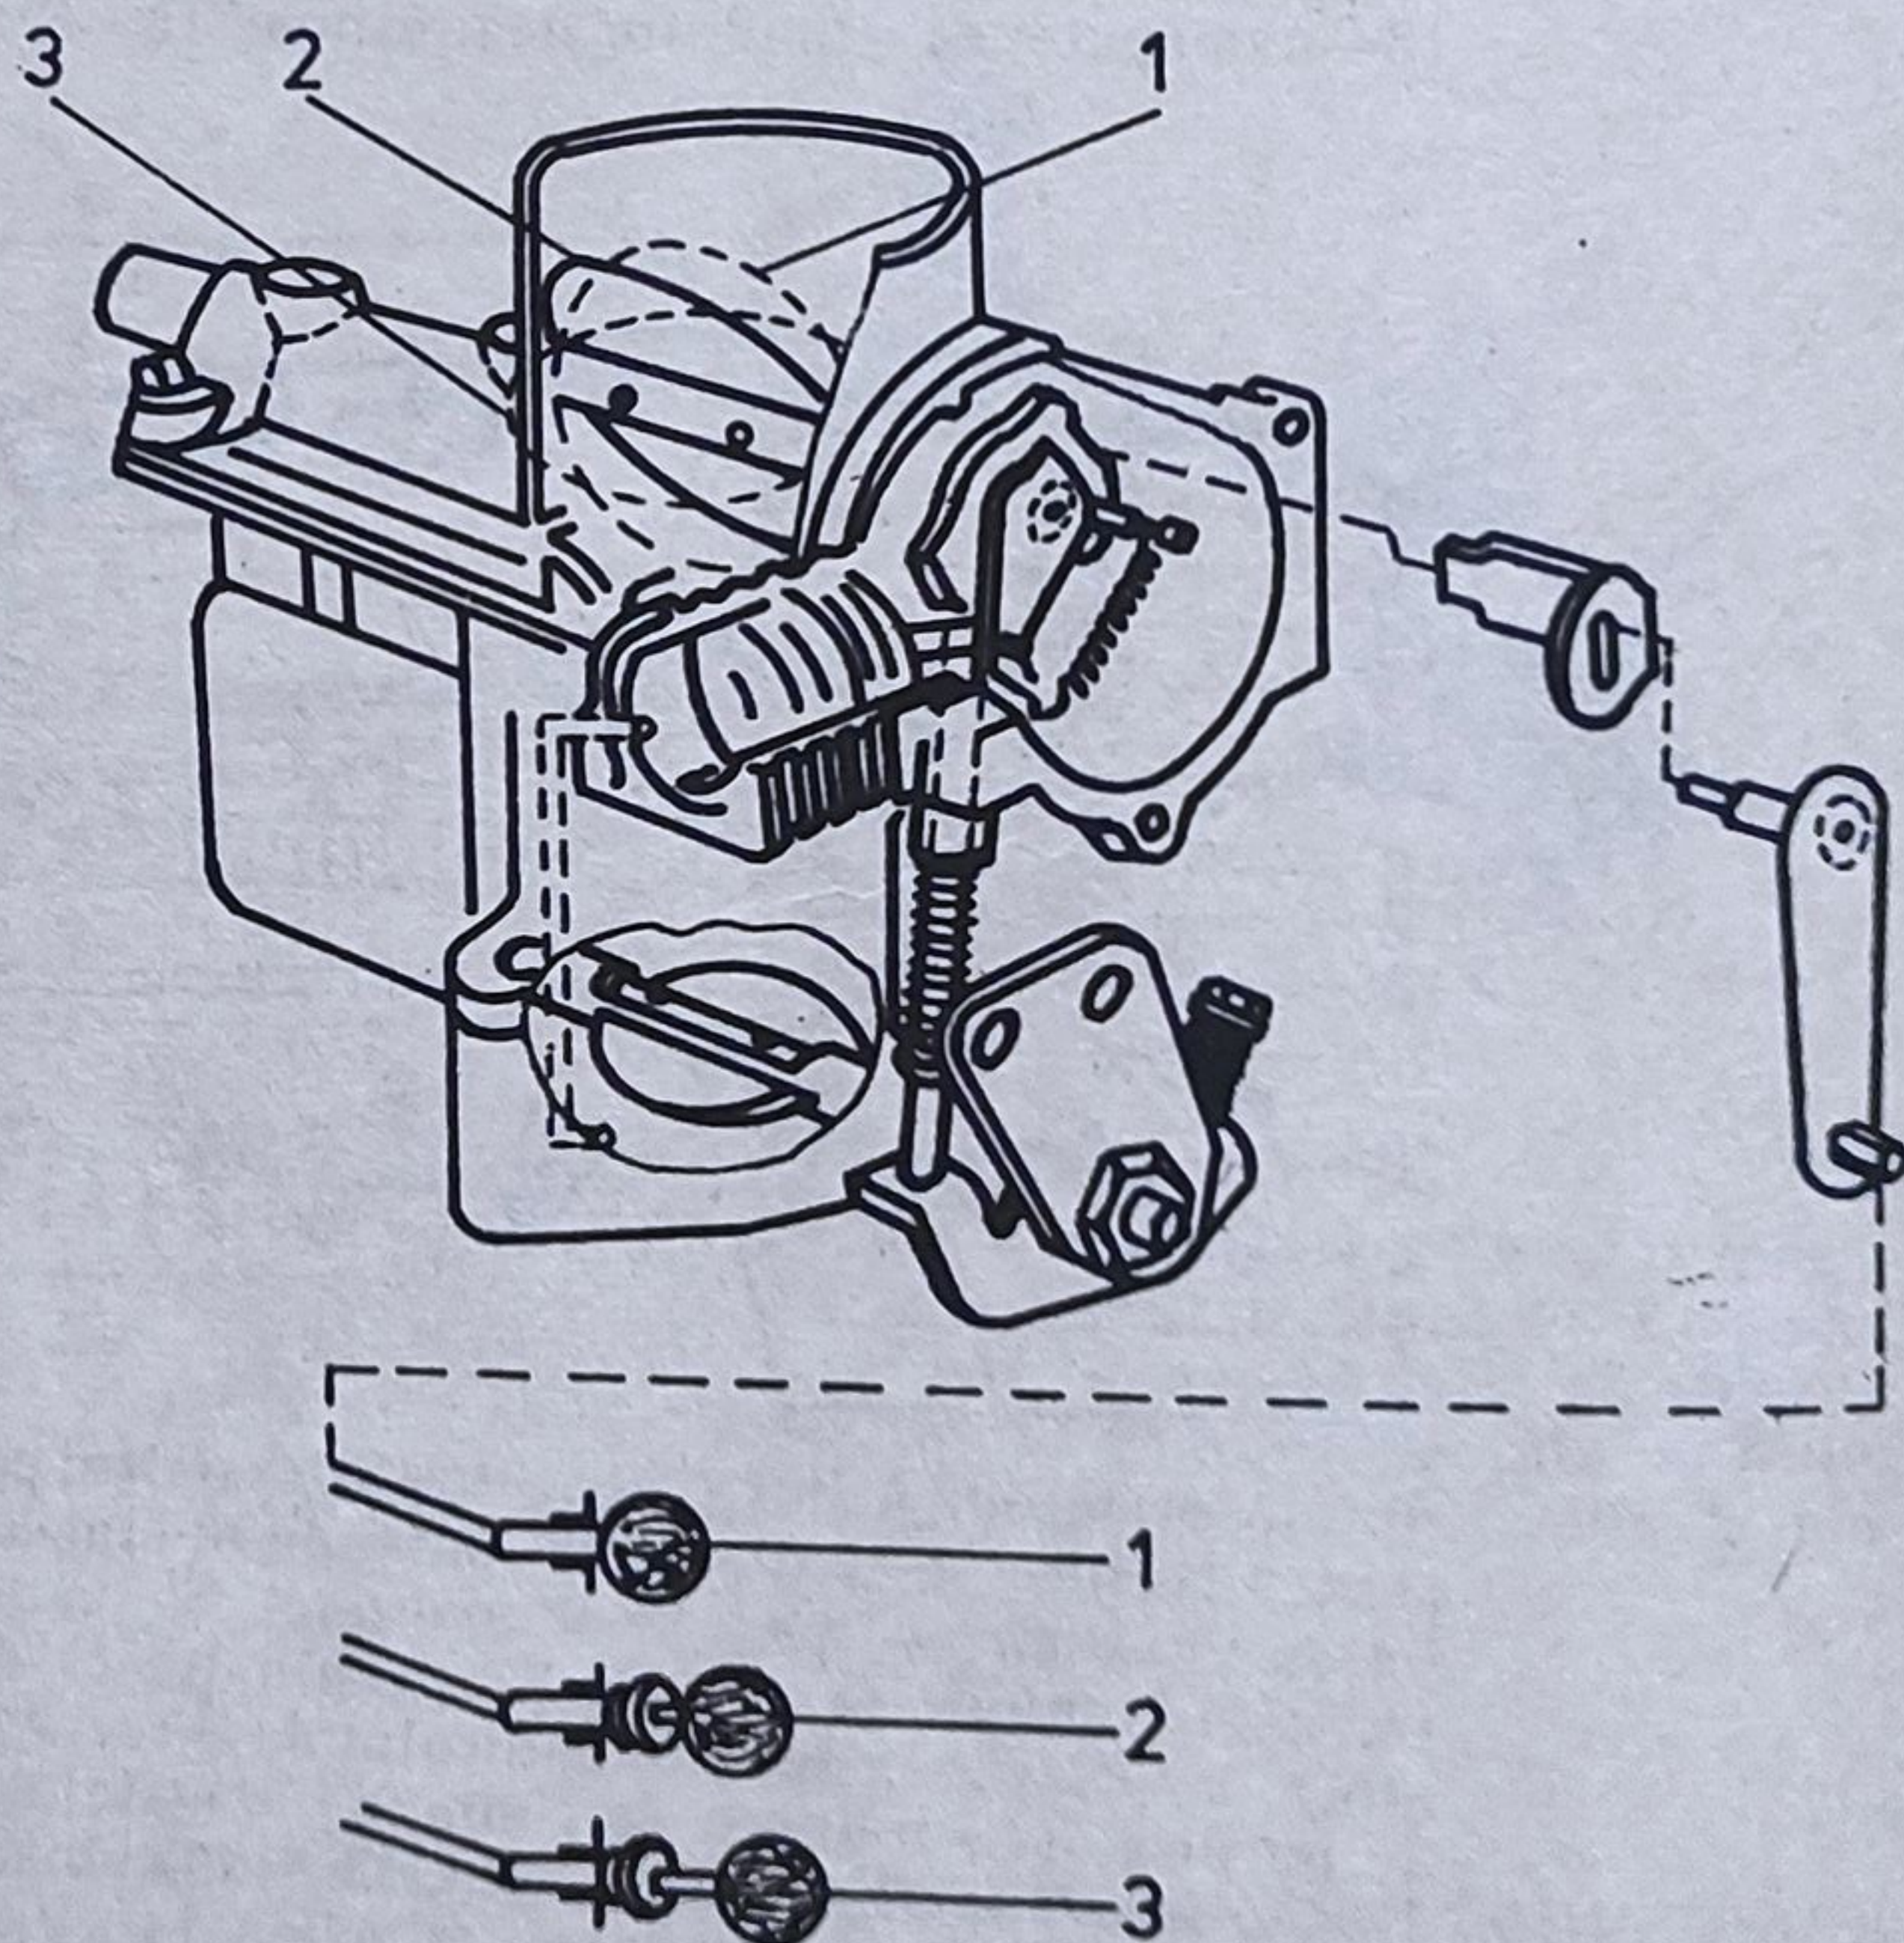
Pozițiile butonului de comandă a clapei de aer: 1 — motorul cald; 2 — motorul semicald; 3 — motorul rece.
